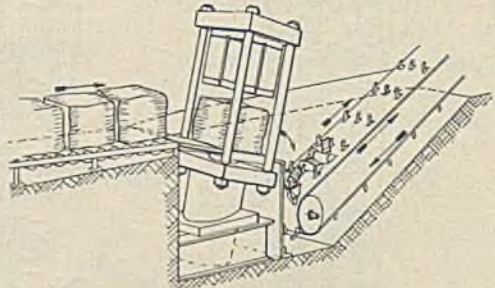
Beschickung und Entleerung einer Ballenschneidermaschine
